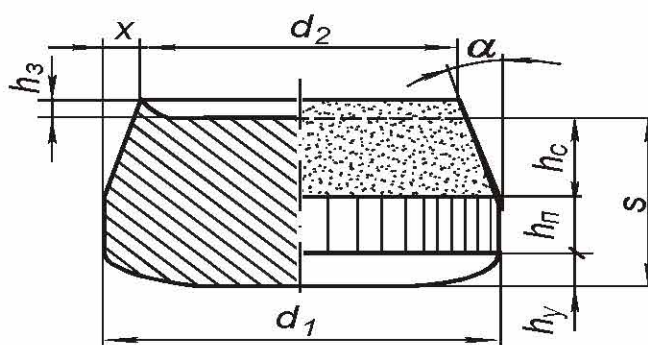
Дефекти бічної поверхні штампованої деталі
